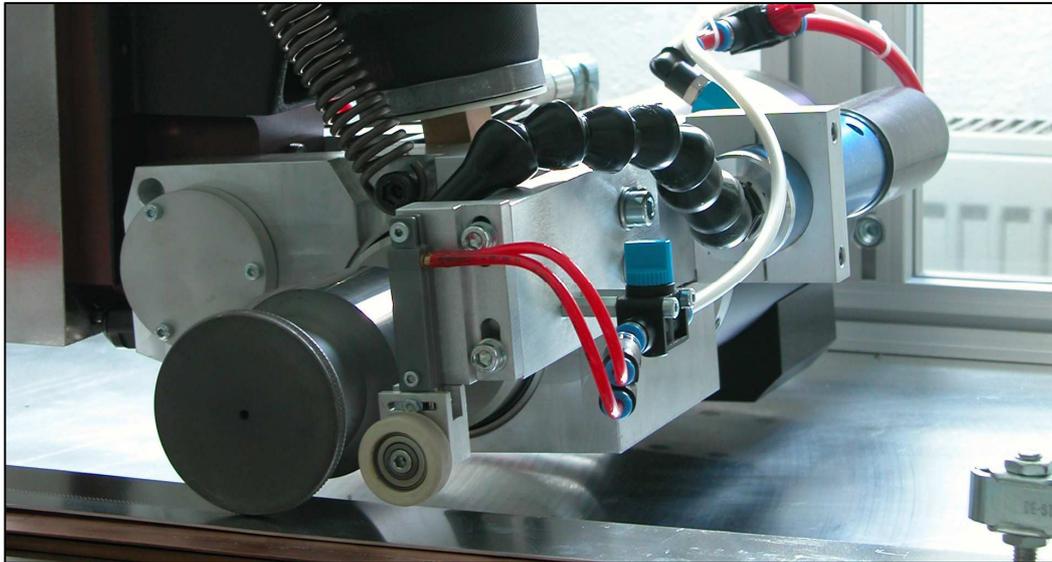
Schweißkopf der Ultraschallrollennaht-Schweißmaschine
